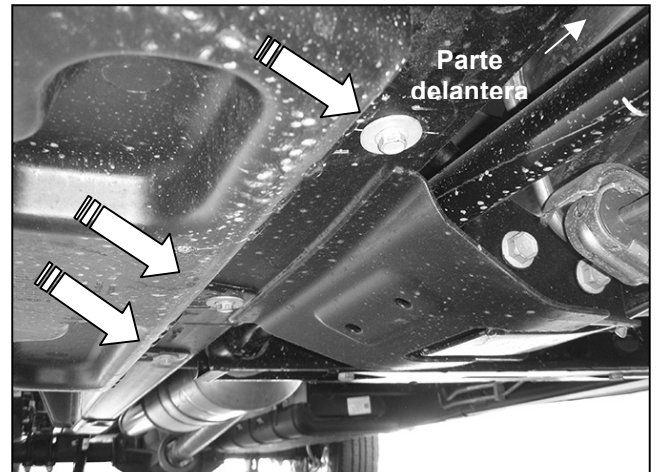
Soportes izquierdo/del lado del conductor instalados
